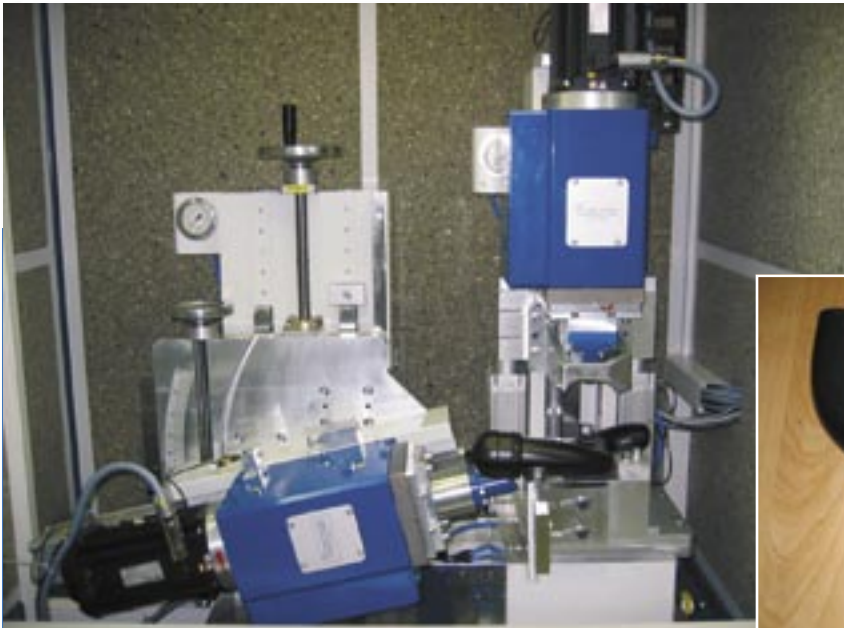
+ 2: Zirkular-Schweißzentrum – die Basismaschine wird um eine Station II erweitert deren Schweißkopf im 3D-Raum einstellbar ist; (Rohrkrümmer der Geiger Technik Thüringen mit 2 Stützen)
